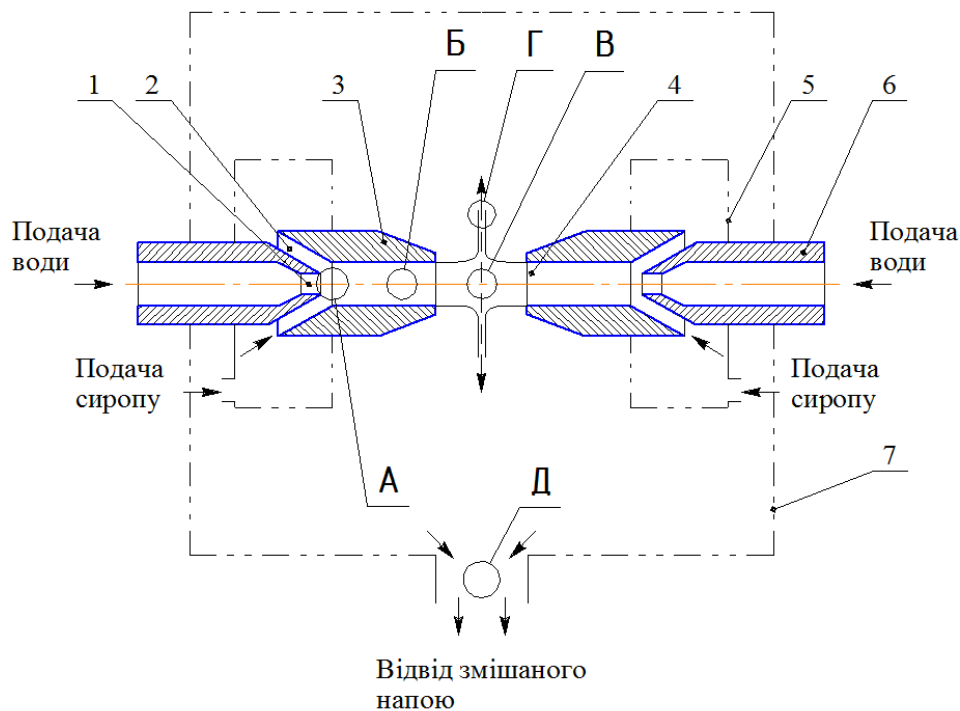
Схема протитечійно-струминного змішувача рідин: 1 – робоче сопло; 2 – приймальна камера; 3 – камера змішування; 4 – сопло камери змішування; 5 – камера подачі підмішуваного компонента; 6 – робочий патрубок; 7 – камера збору рідини. А, Б, В, Г, Д – зони змішування
